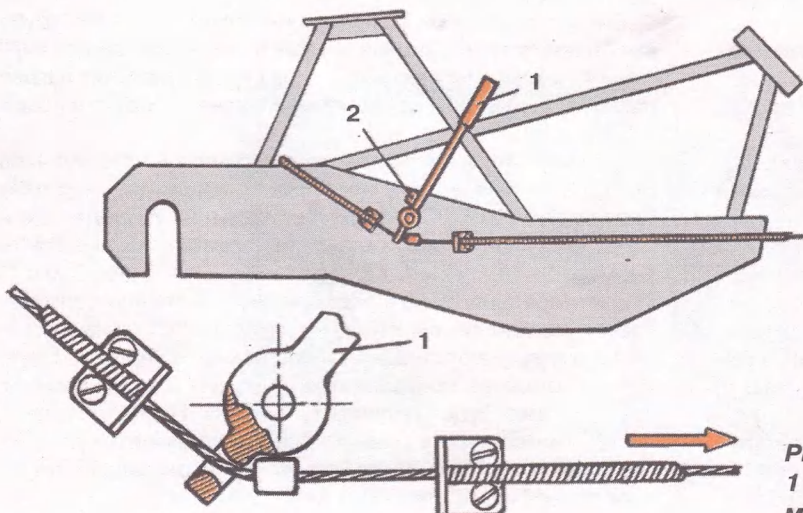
Стояночный тормоз: 1 — рычаг стояночного тормоза; 2 — фиксатор рычага.
